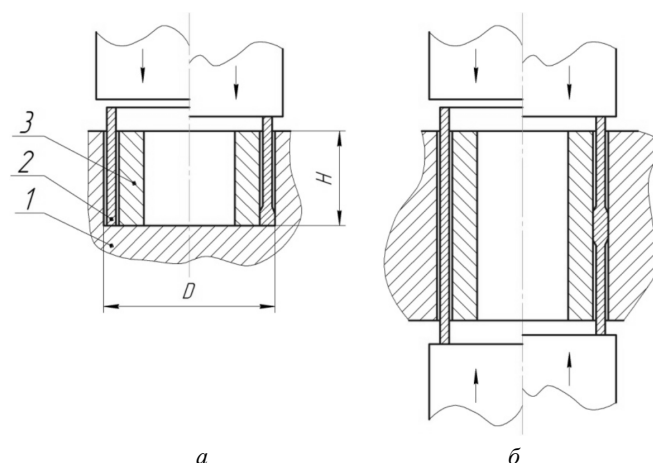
Сборка прессового соединения с промежуточной втулкой
